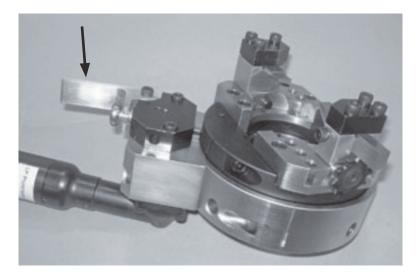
Ce levier permet d'engager et de rétracter le déclencheur de l'arrière de la machine sans vous placer dans l'espace des pièces mobiles.
